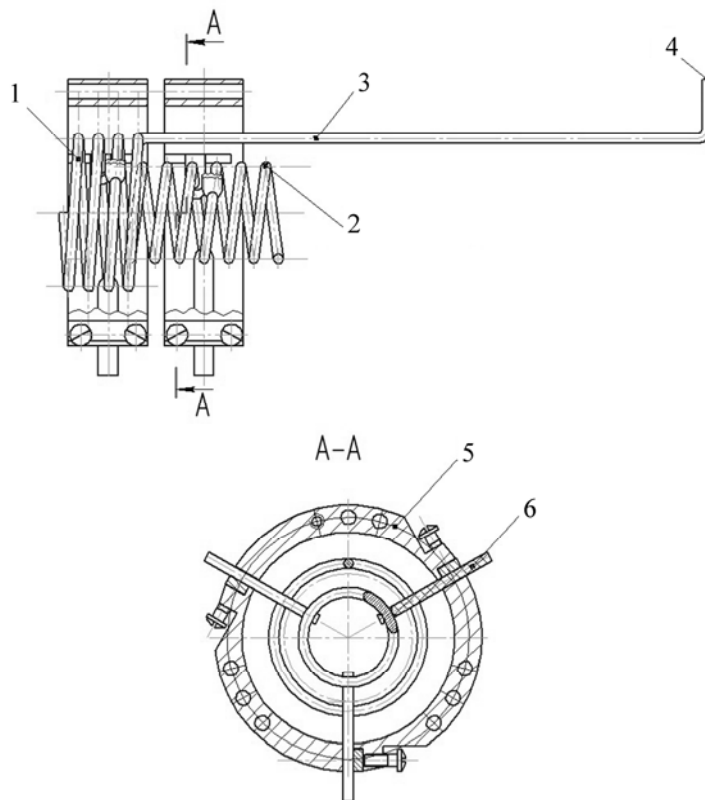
Эскиз ЗС типа ЦССР без внешнего корпуса: 1 – отрезок спирали УВЭ; 2 – спиральный резонатор (со стороны электронной пушки); 3 – вывод УВЭ; 4 – сечение подключения коаксиального кабеля; 5 – кольцо корпуса ЗС; 6 – фторопластовая опора
